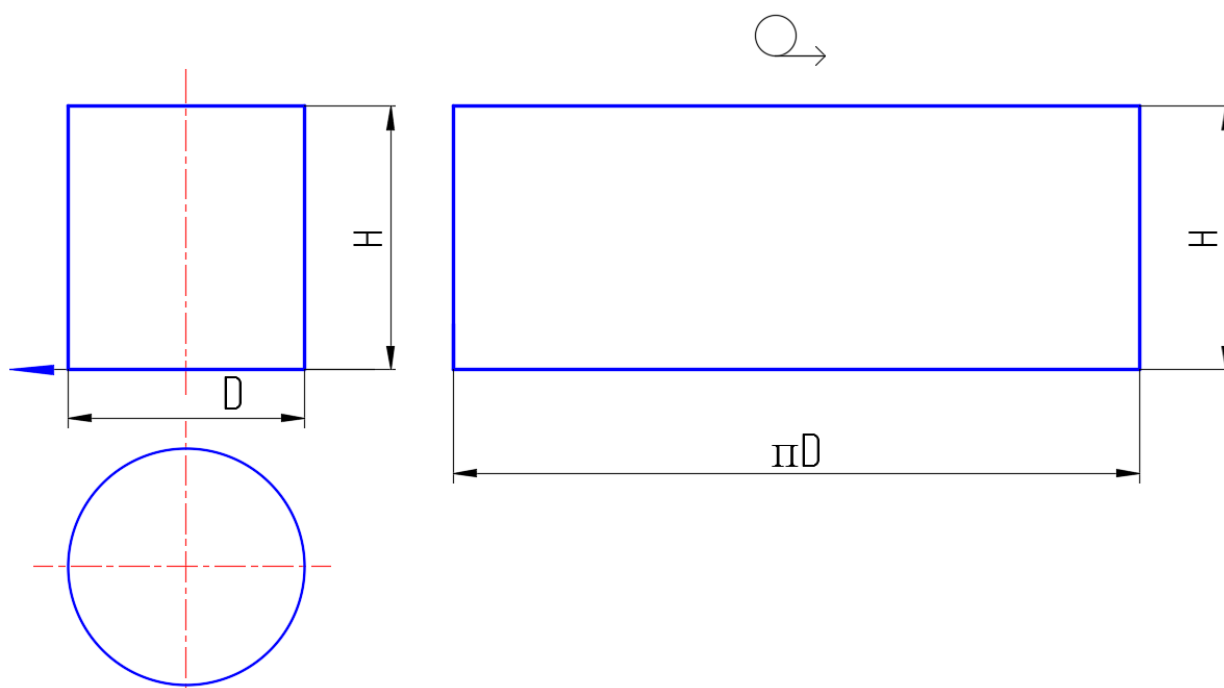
Точная развертка боковой поверхности цилиндра вращения
